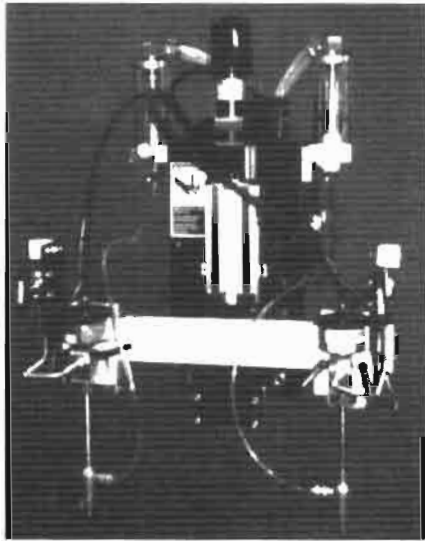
Устройство для гидроабразивной резки двумя головками
